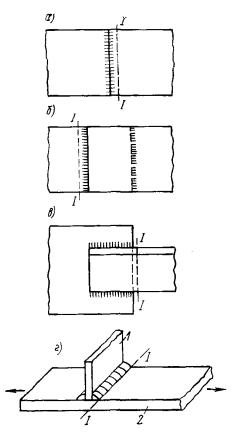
Конструкции и схема сварных соединений a — встык; δ — внахлестку лобовыми швами; s — внахлестку фланговыми швами; s — схема прикрепления поперечного элемента к элементу, не имеющему стыка; I — поперечный элемент; 2 — элемент без стыка; I — I — расчетное сечение
